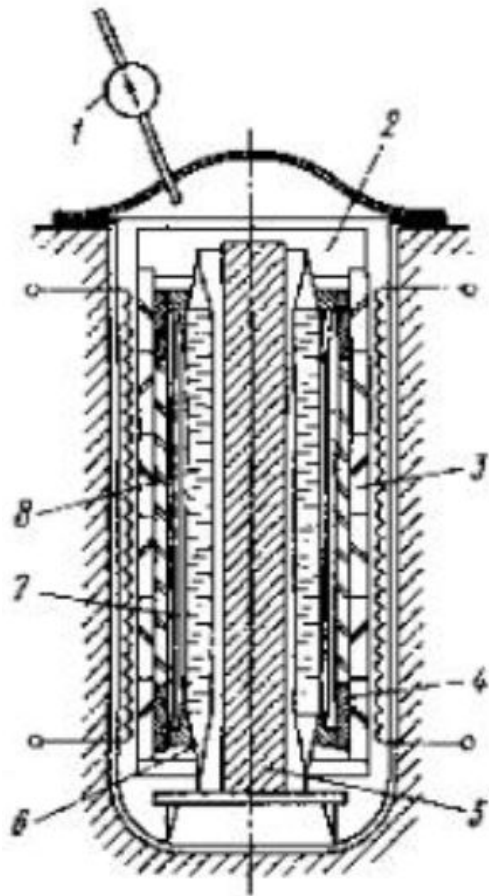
а) схема паростата: 1 – вакуумный насос; 2 – вакуумная печь; 3 – кольцевые обоймы; 4 – законцовка трубчатой балки; 5 – оправка; 6 – формирующая замкнутая оболочка; 7 – бороалюминиевый полуфабрикат; 8 – цулаги;
